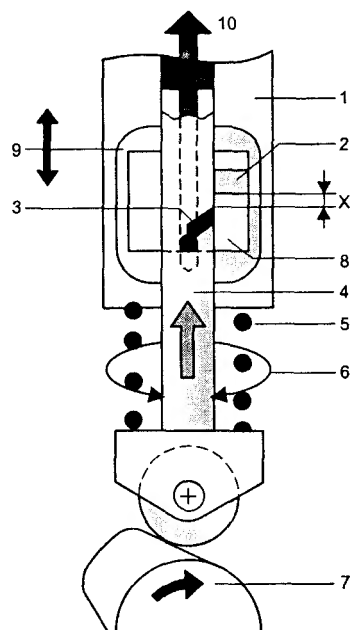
Система впрыска с рядным ТНВД с дополнительной втулкой: 1 — гильза плунжера; 2 — впускное окно; 3 — регулирующая кромка плунжера; 4 — плунжер; 5 — возвратная пружина плунжера; 6 — поворот плунжера регулирующей рейкой; 7 — кулачковый вал; 8 — дополнительная втулка; 9 — изменение хода плунжера за счет регулирующей втулки; 10 — подача топлива к форсунке; X — активный ход плунжера
